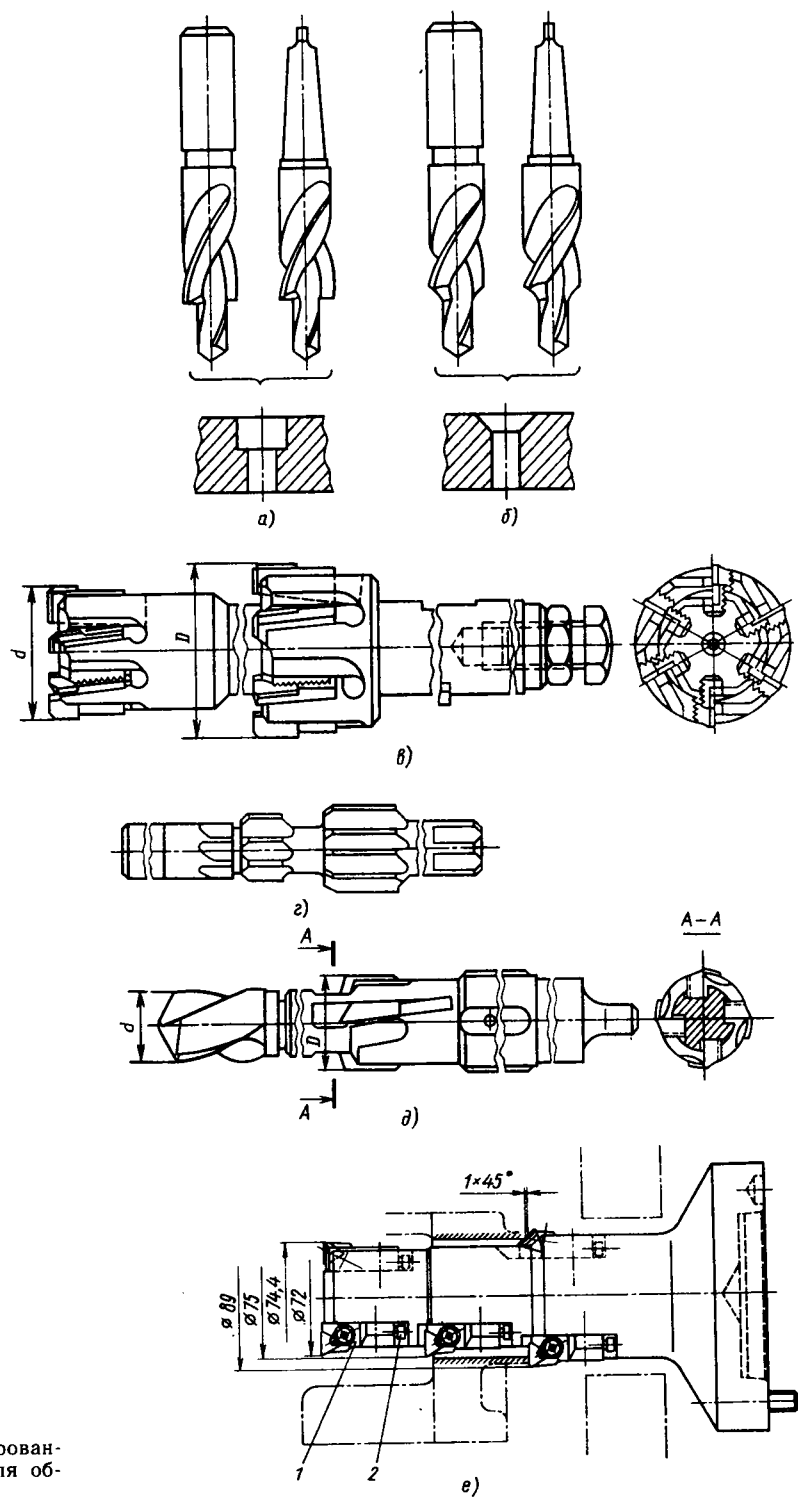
Комбинированные инструменты для обработки отверстий
